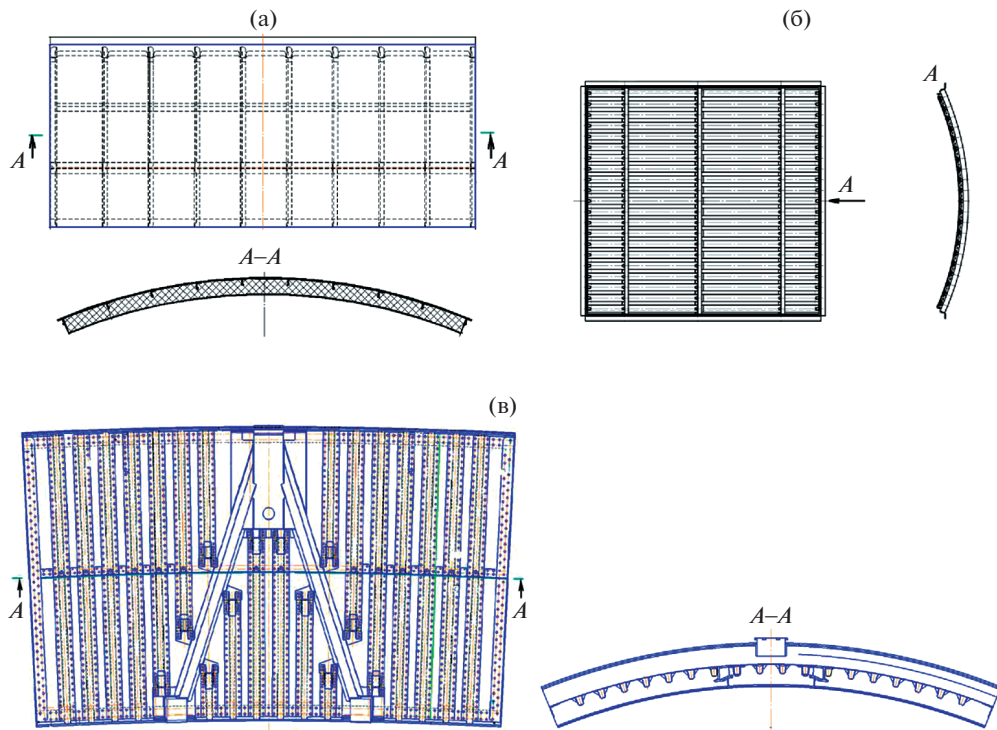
Образцы для испытаний: (а) – образец 1; (б) – образец 2; (в) – образец 3.
